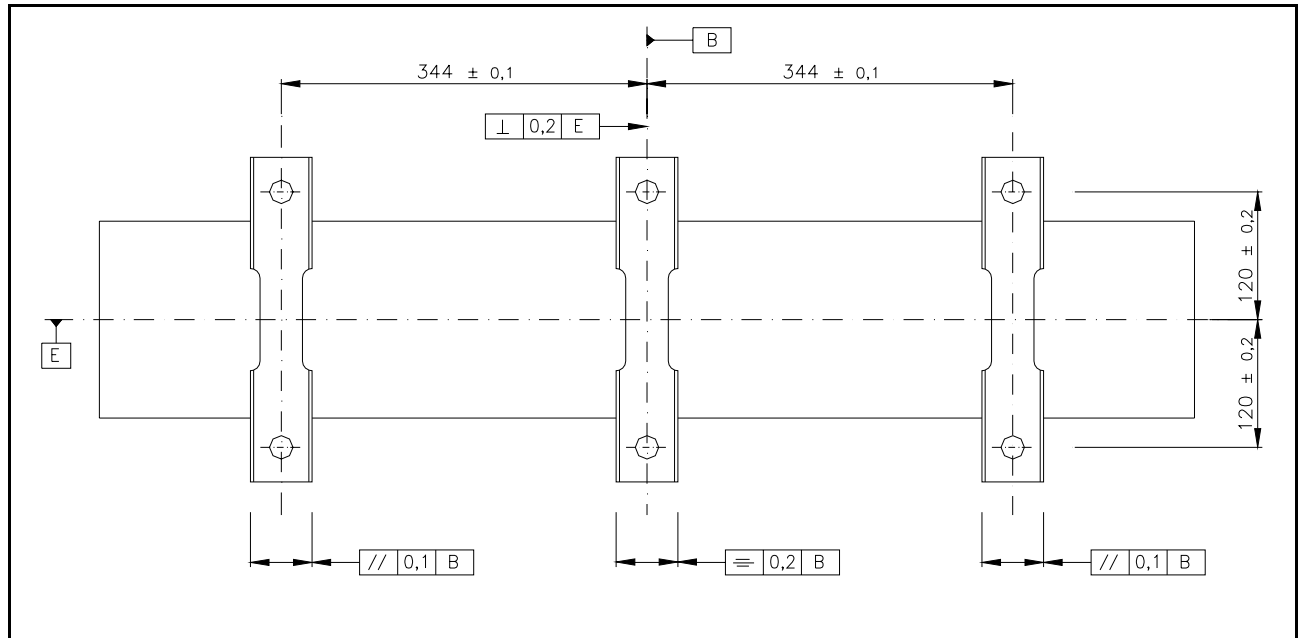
Befestigungsachsen des Statorpaketes (Draufsicht)
